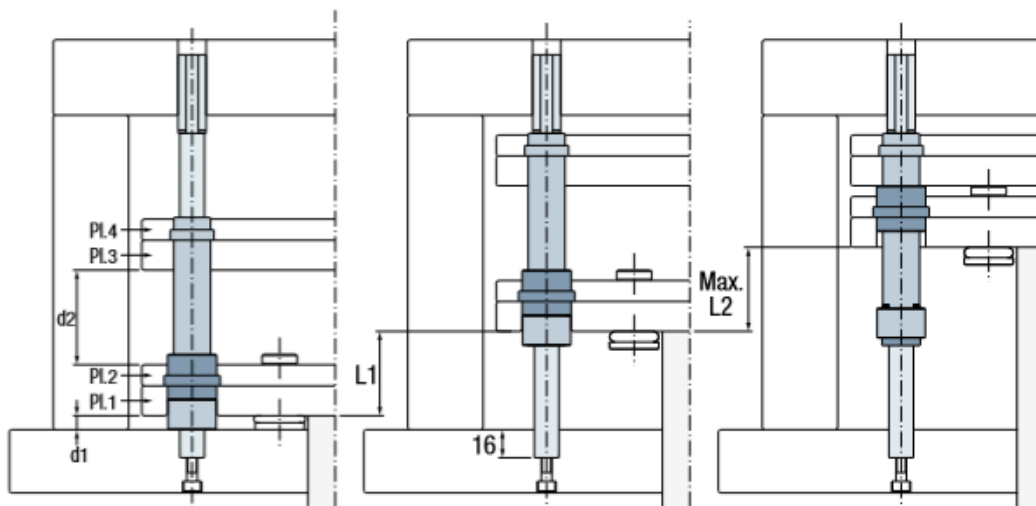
Esquema de la doble expulsión. Techno Injection & Tools
